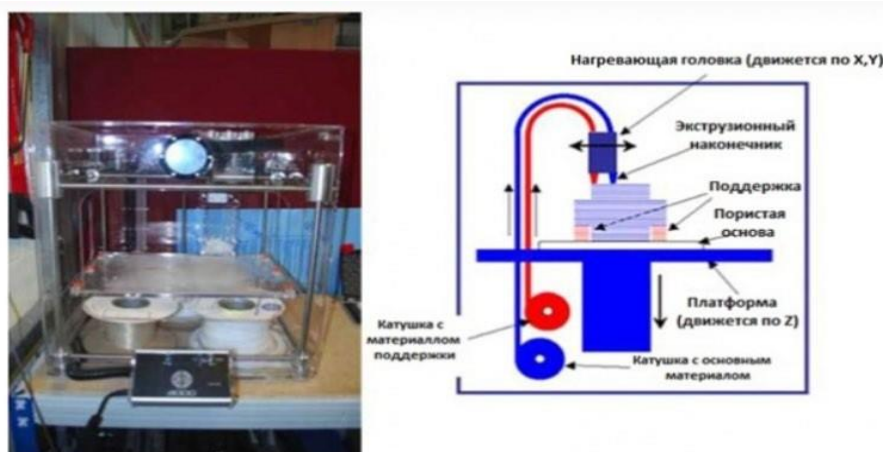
Общий вид и схема работы типичного FDM – принтера
